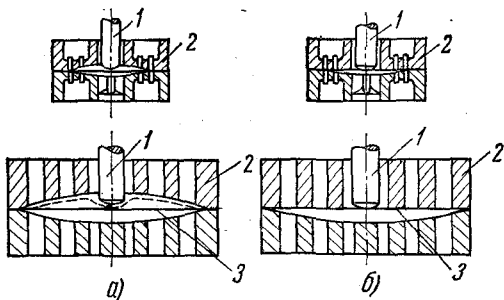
Схема расположения мембраны и суппортов у датчиков старой и усовершенствованной конструкции
